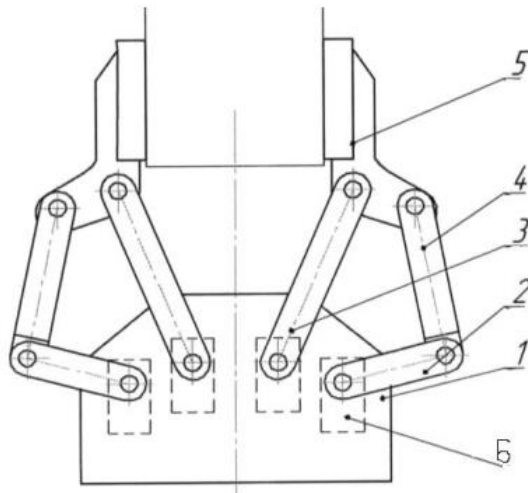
' Адаптивний захватний пристрій'. [24]
